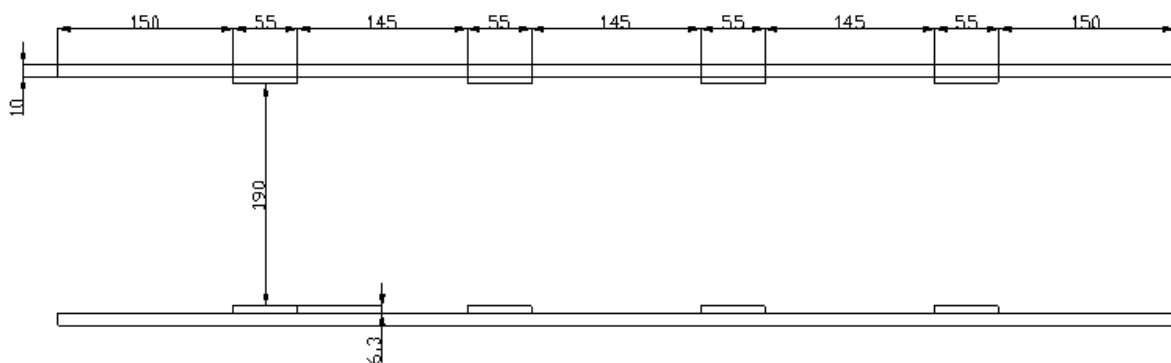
Схема пристрою для магнітної обробки картоплі
